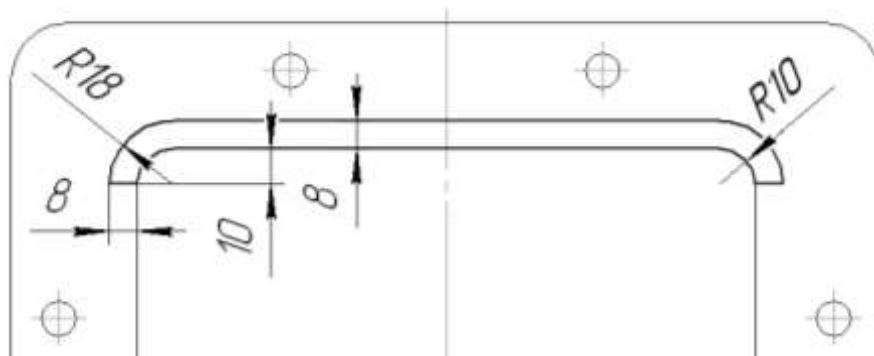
Ескіз профілю передньої стінки редуктора
